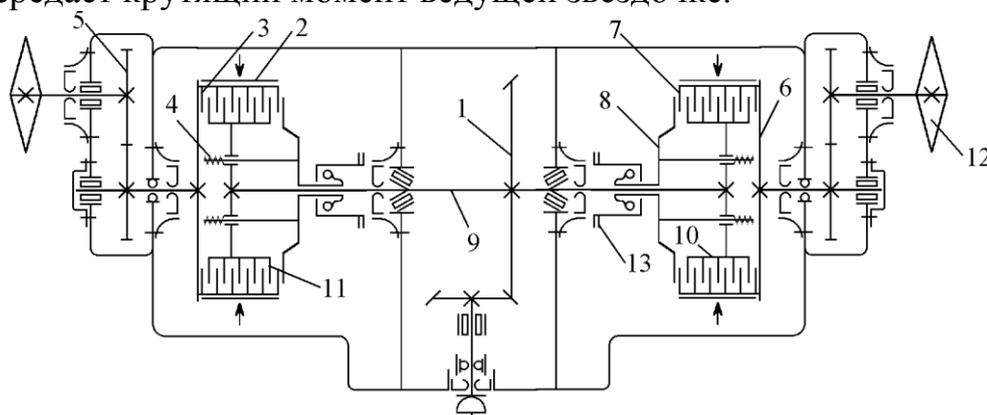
Многодисковая муфта поворота: 1 – главная передача; 2 – ленточный тормоз; 3 – опорный диск; 4 – пружина; 5 – бортовая передача; 6 – ведомый барабан; 7 – ведомые диски; 8 – нажимной диск; 9 – поперечный вал; 10 – ведущий барабан; 11 – ведущие диски; 12 – ведущая звездочка; 13 – механизм выключения
